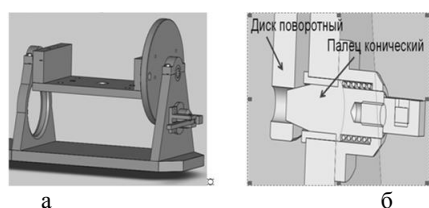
а – общий вид поворотного механизма, б – механизм фиксации поворотного диска
